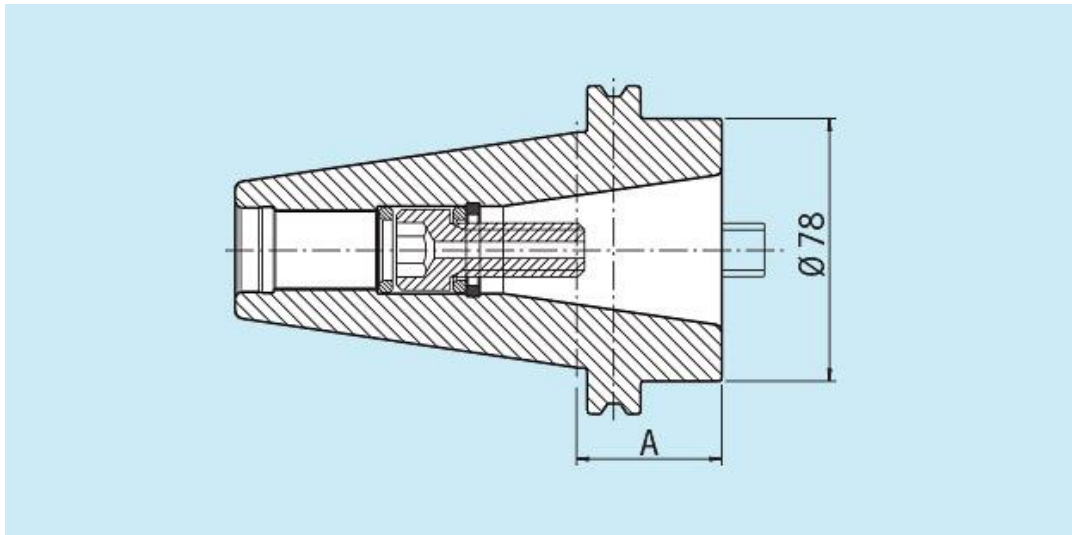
Інструментальний конус SK50 в розрізі [10]
